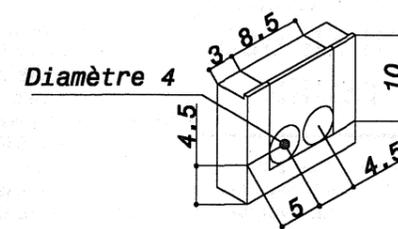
Serrer la pièce horizontalement et percer 2 trous de 4 mm.
